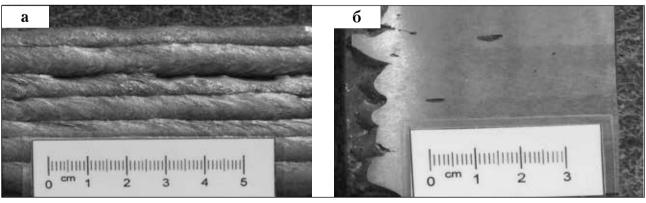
Внешний вид наплавленной поверхности с неравномерным усилением наплавленных валиков и недостаточным перекрытием соседних валиков (514) после наплавки (а) и после механической обработки (б) [6]
